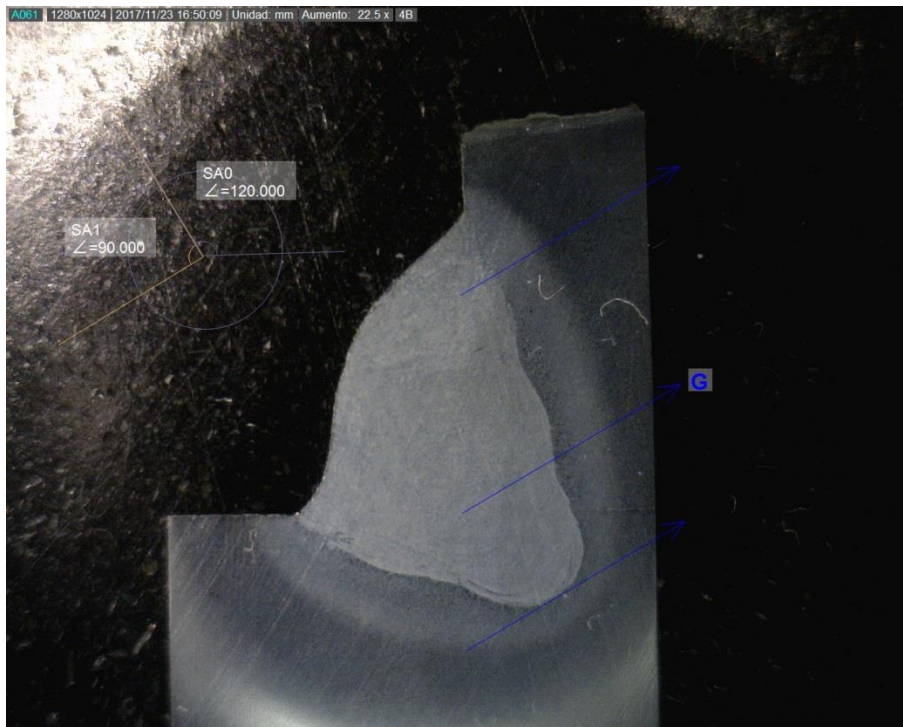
9 Perfil obtenido en cupón de soldadura 5A.
